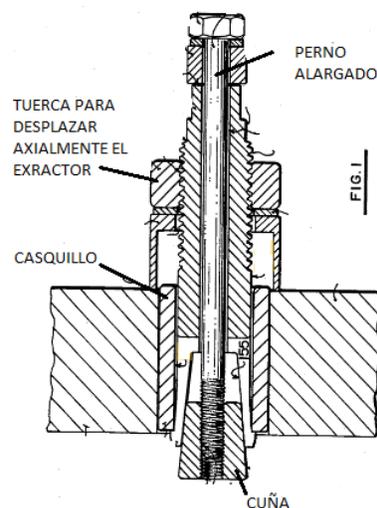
Herramienta de extracción para cojinetes, casquillos y similares.
